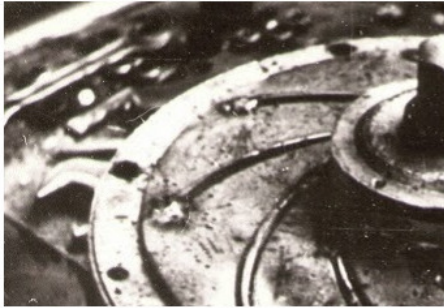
Составные части рабочего колеса центробежного насоса бНДв в кондукторе для сборки
